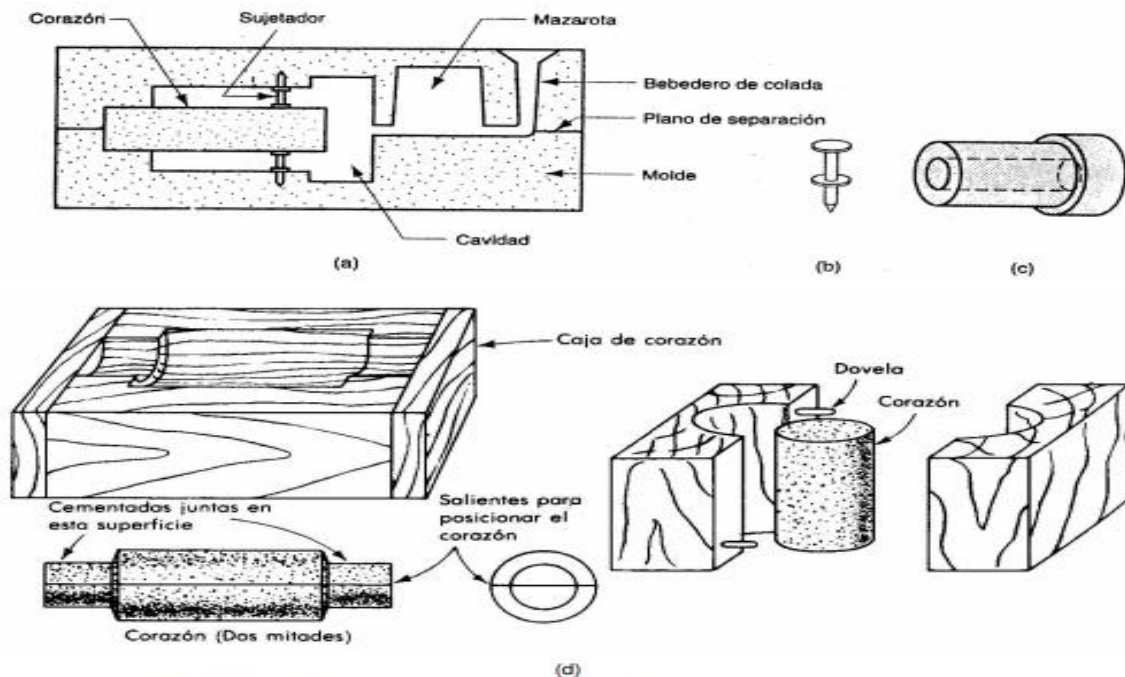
(a) corazón mantenido en su lugar dentro de la cavidad del molde por los sujetadores (b) Diseño posible del sujetador (c) Fundición con cavidad interna (d) manufactura del corazón
